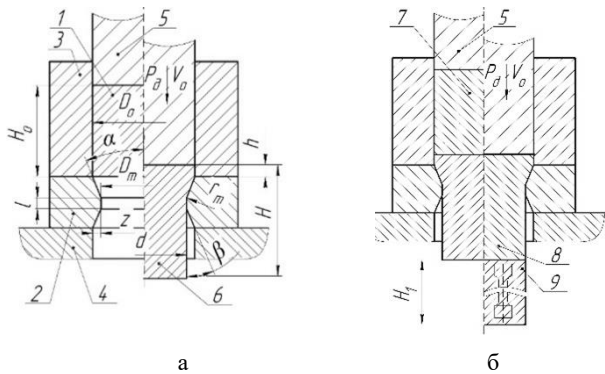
Виготовлення деталі прямим видавлюванням по схемі «заготовка за заготовкою»: а – схема видавлювання першої заготовки, б – схема видавлювання другої заготовки
